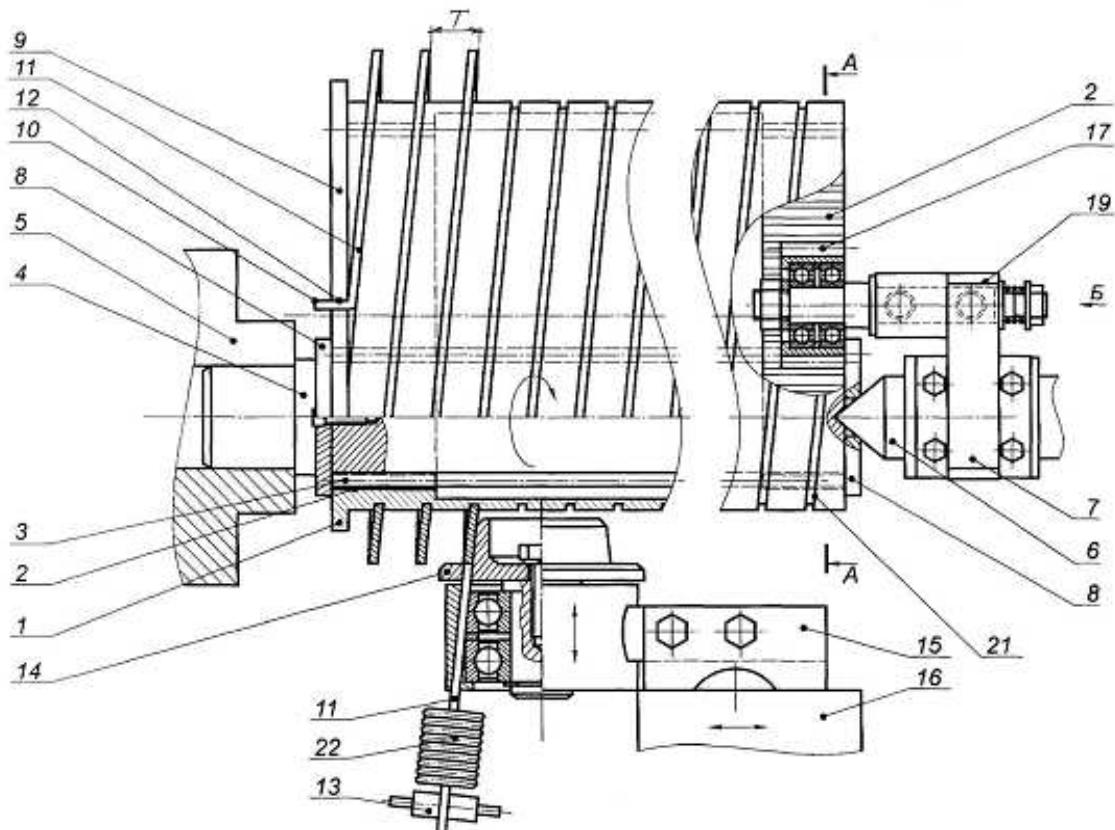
Пристрій для виготовлення гвинтових еліпсних заготовок
